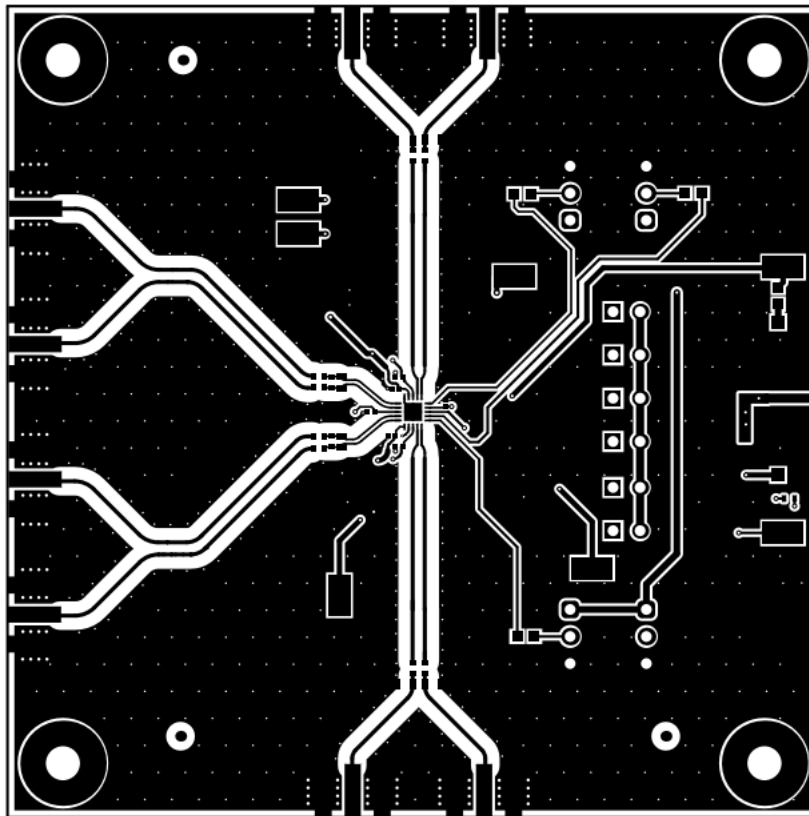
顶层 (CLKIN / CLKOUT 信号)
